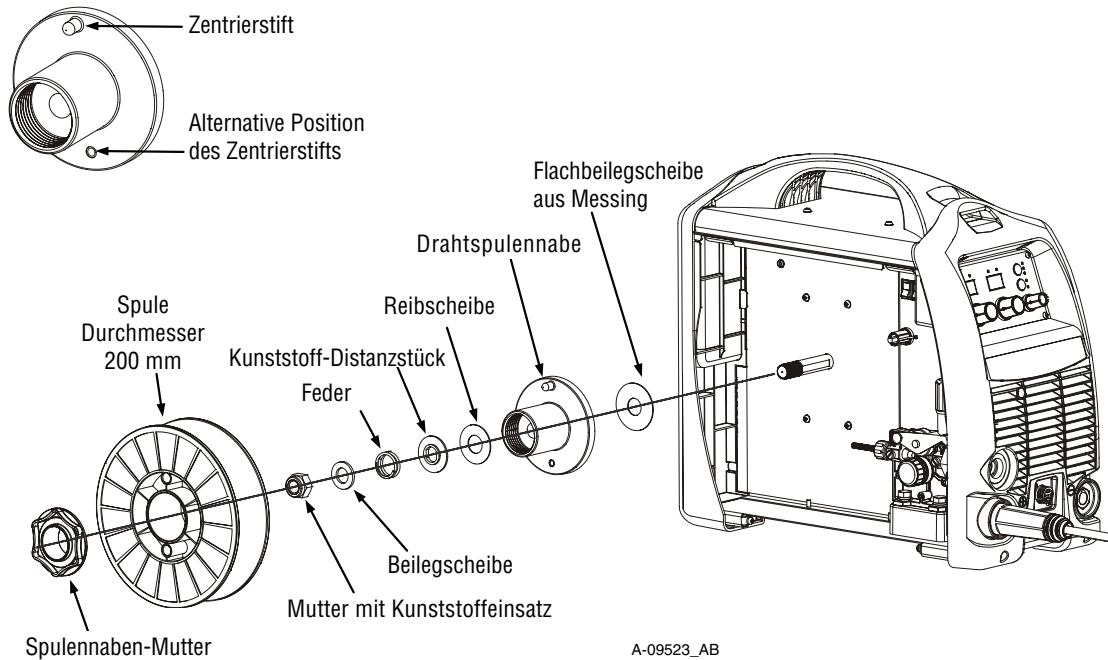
Einbau einer Spule mit 200 mm Durchmesser
